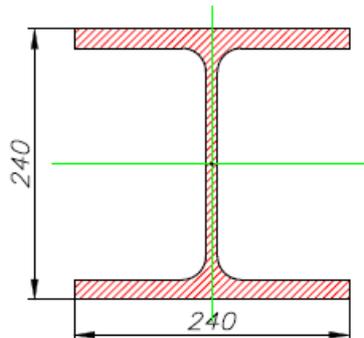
Sección transversal viga Stand Reel. Fuente: (Autor)
